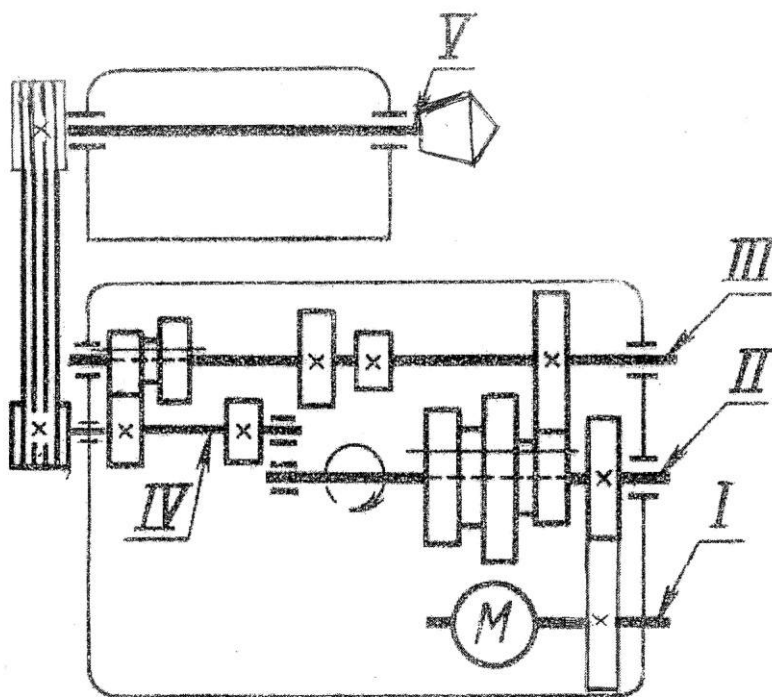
Кинематическая схема бабки токарно-винторезного станка мод. 1616
